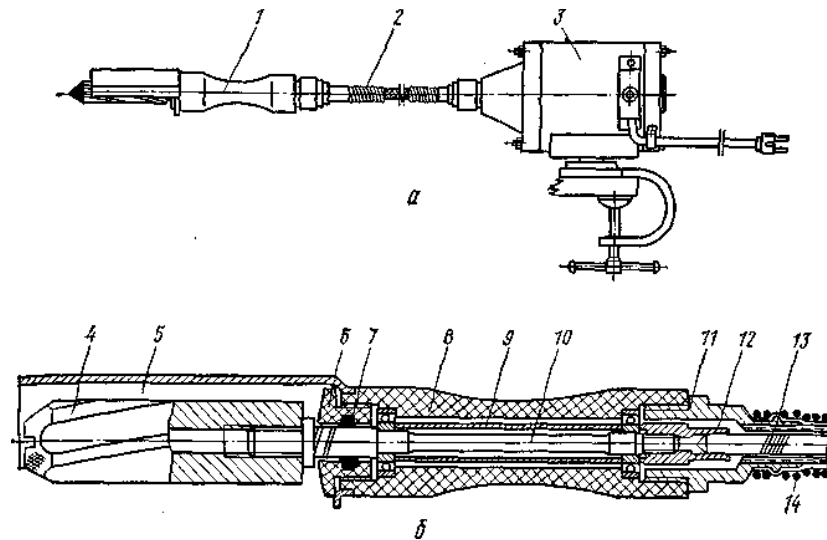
Пристосування РО-1М для очистки риби:
